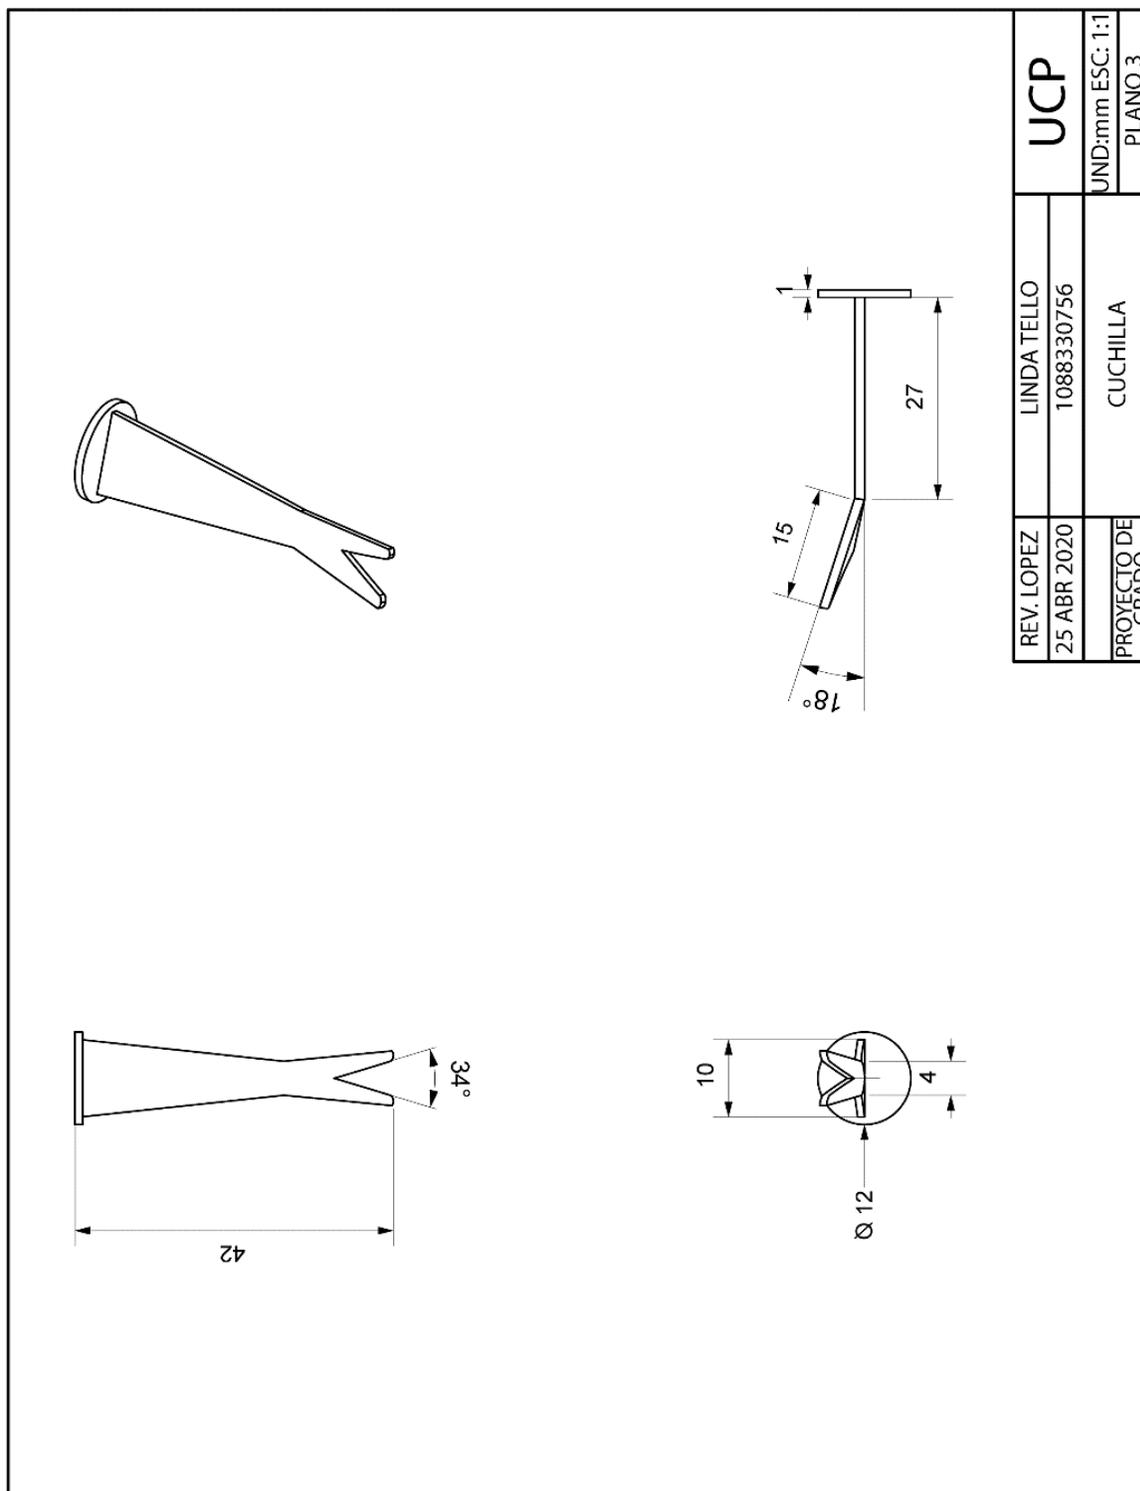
Plano de cuchilla. Fuente: Elaboración propia
